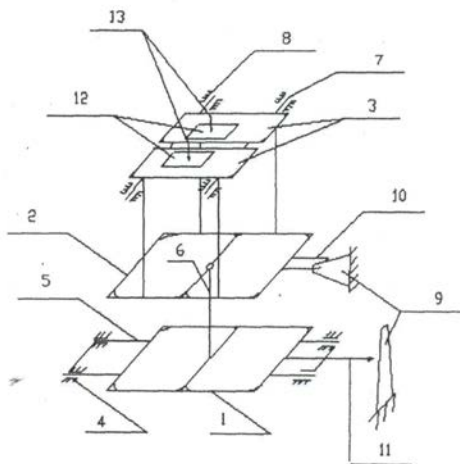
Схема сборочно-сварочного приспособления для сварки трением вращающимся инструментом:
